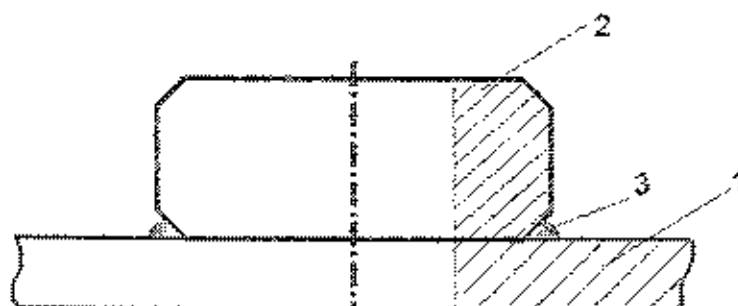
Увеличение длины свинчивания при помощи приварки гайки: 1-гайка; 2 – заготовка; 3- сварной шов [3]
